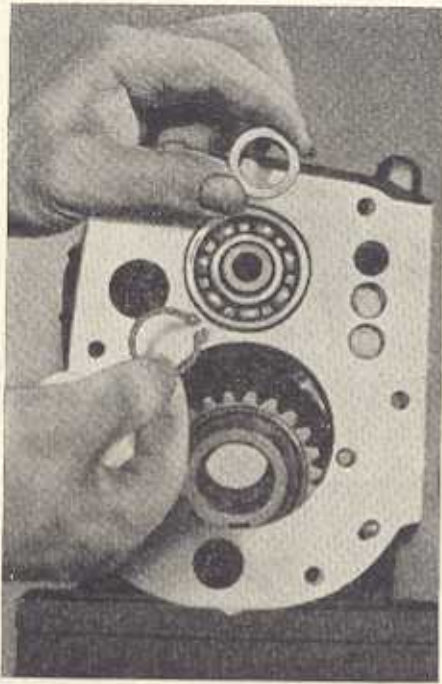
Abnehmen des Sicherungsringes für hinteres Rillenkugellager der Antriebswelle
